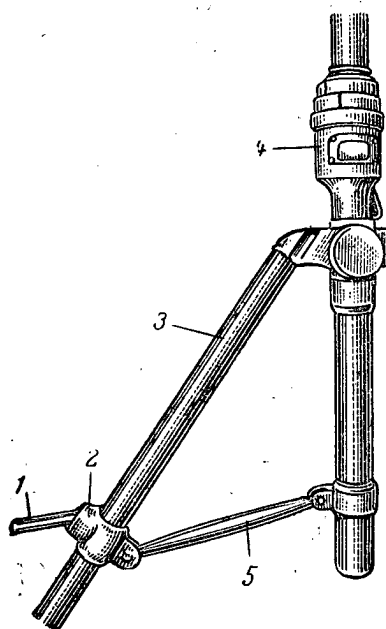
Механизм грубого горизонтирования: 1 — вороток; 2 — зажимная втулка; 3 — нога двуноги; 4 — корпус подъемного механизма; 5 — тяга
